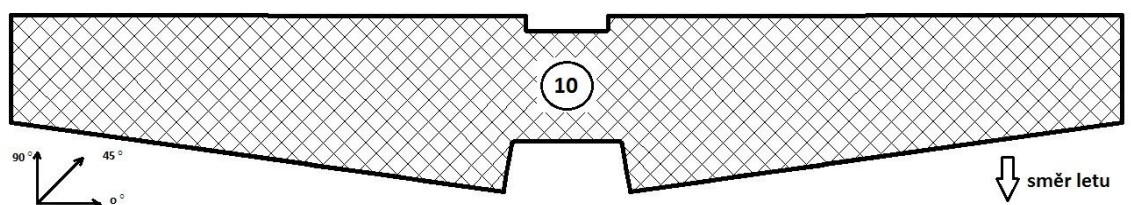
Vrstvení potahu stabilizátoru – zadní výztuhy, vrstvy č. 6, 7, 8
